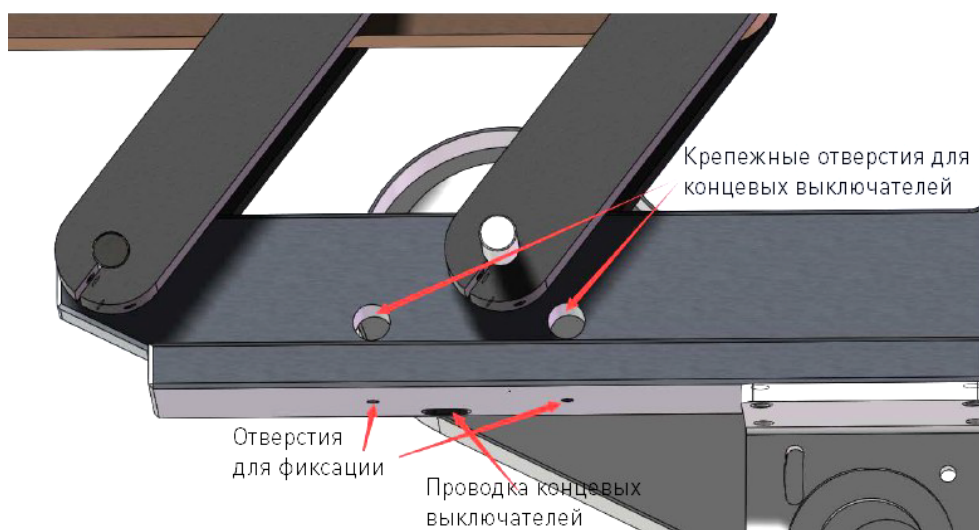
Схема установки концевых выключателей для оси движения вперед-назад.
